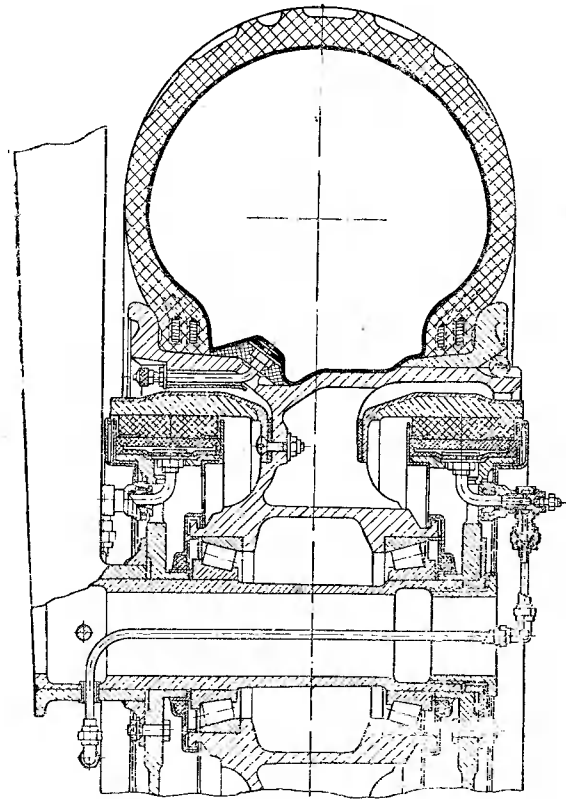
Установка колеса с двумя камерными тормозами на шасси консольного типа
